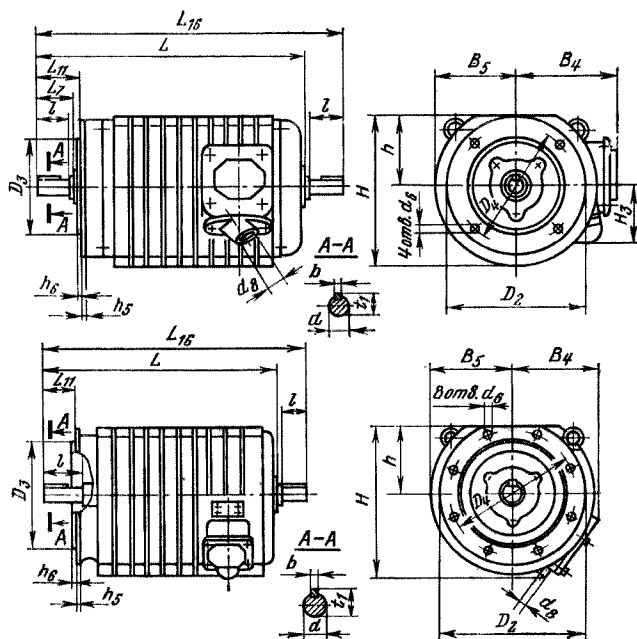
Габаритные и установочные размеры двигателей серии АРФ 4—7-го габаритов.
